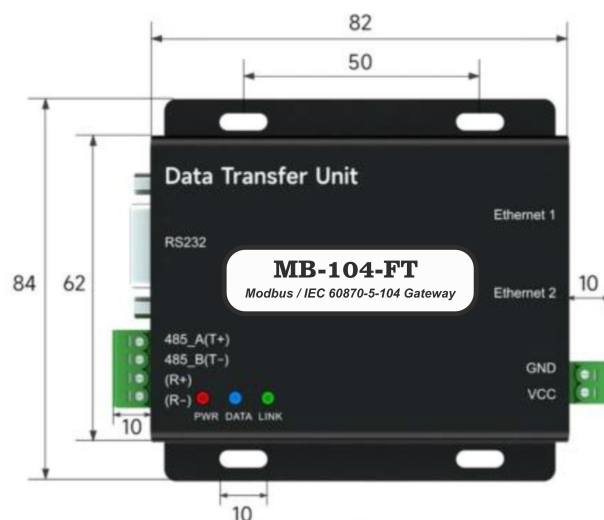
Габаритные и присоединительные размеры MB-104-FT.
